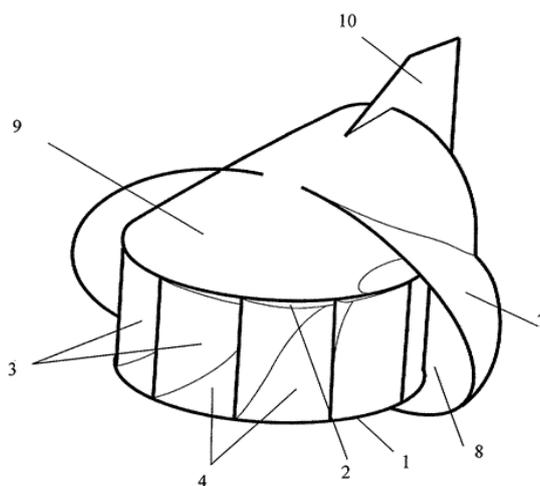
Ветроустановка Третьякова (общий вид установки): 1 – нижнее основание; 2 – верхний элемент корпуса; 3 – пространственные лопасти; 4 – рабочий канал направляющего аппарата; 5 – центральный выходной канал корпуса; 6 – рабочее колесо; 7 – воздухозаборник; 8 – внутренняя полость воздухозаборника; 9 – сопло; 10 – стабилизатор
